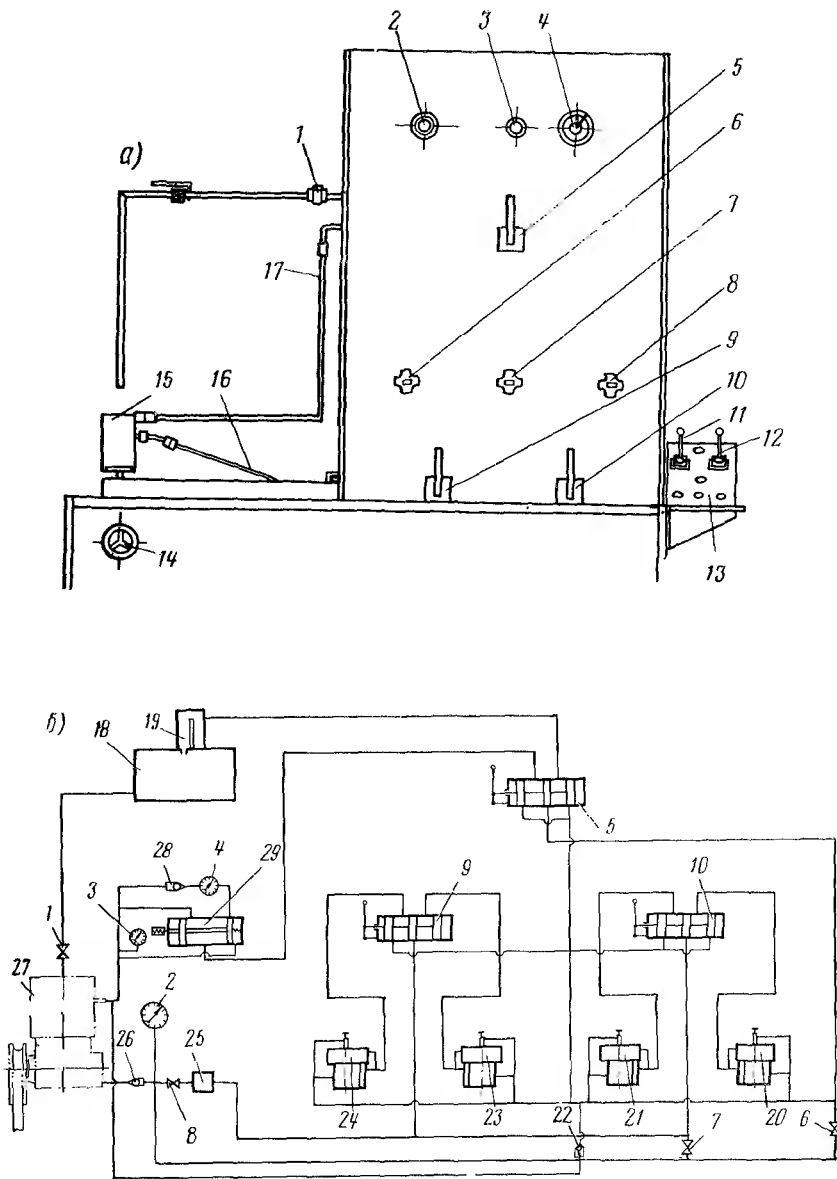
Стенд для испытания насоса гидроусилителя рулевого управления:
